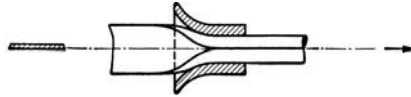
Stumpfschweißung durch Ziehen.
